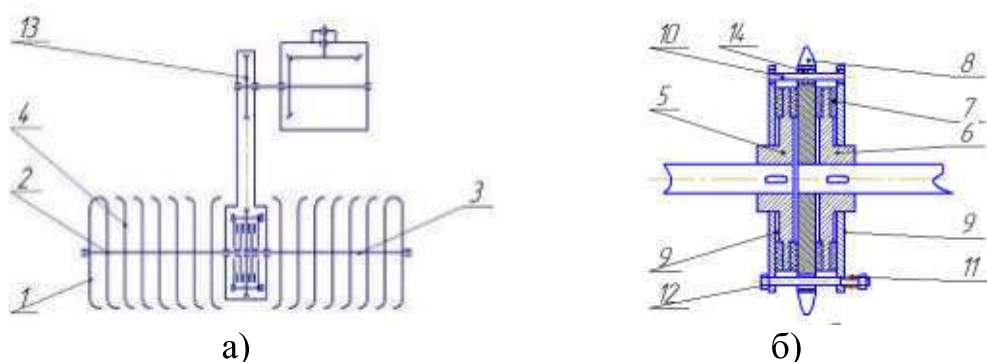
Конструктивно-технологическая схема лесной фрезерной машины с двухпоточным предохранительным устройством с центральным приводом (рис. 5, а) и двухпоточный предохранитель (рис. 5, б):
